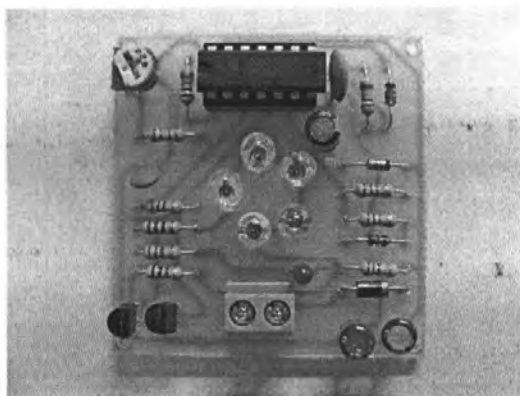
แสดง PCB ของวงจรภาครับของ Sensor
